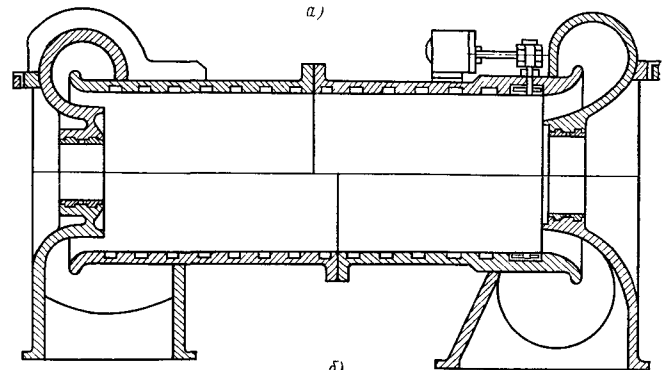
Корпус компрессора, отлитый как одно целое с патрубками ГТУ фирмы Броун — Бовери
